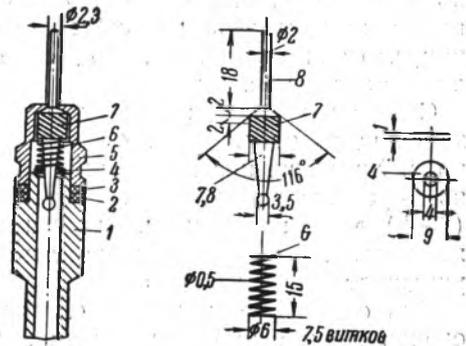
Приспособление ранцевого опрыскивателя для нефтевания яйцекладок непарного шелкопряда:
